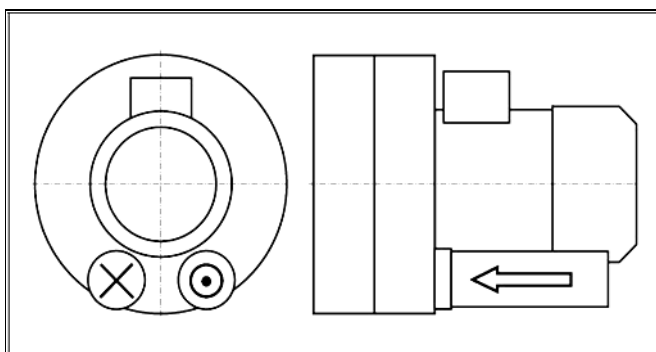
Двухпоточная конструкция вакуумного насоса/компрессора с двумя рабочими колесами.
